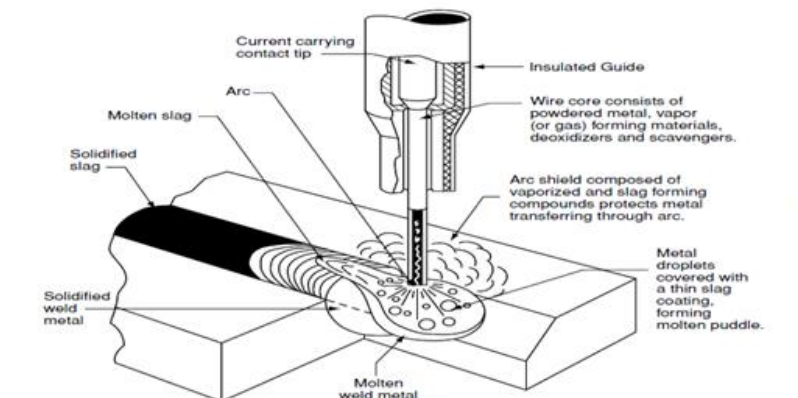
Processo de soldadura com fio fluxado auto protegido (114) [11].
